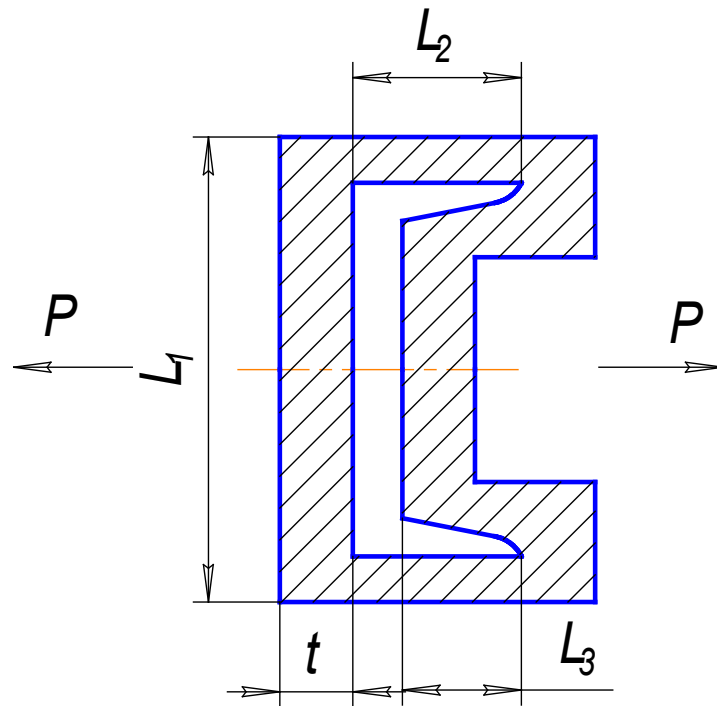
Розрахункова схема зварювального кріплення кронштейна до рами
